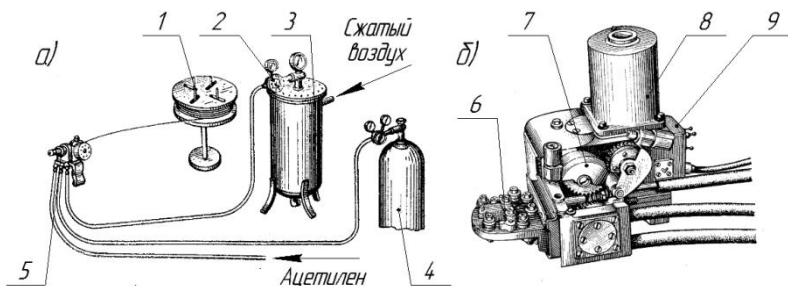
Установка для газовой металлизации (а) с металлизатором ЭМ-6 (б):
